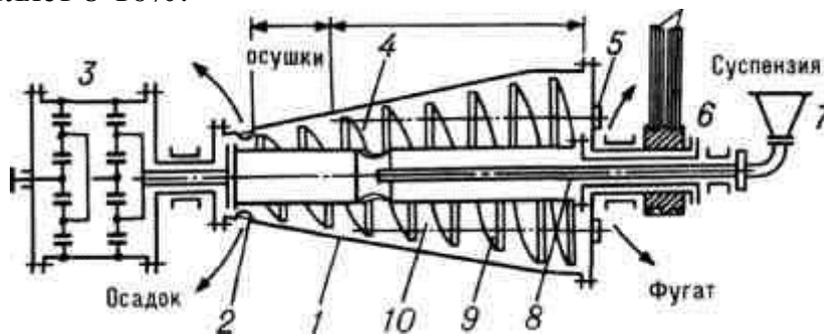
Схема осадительной центрифуги: 1 – рабочий барабан, 2,4,5 – разгрузочные, питающие и сливные окна, 3 – планетарный редуктор, 6 – шкив, 7 – загрузочная воронка, 8 – питающая труба, 9,10 – шнек и шнековый барабан
